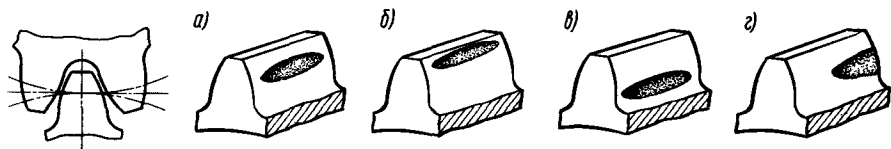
Отпечаток краски при регулировке зацепления зубьев колес цилиндрической зубчатой передачи: а — при нормальном зацеплении; б — при большом боковом зазоре; в — при малом зазоре; г — при перекосе зубьев
